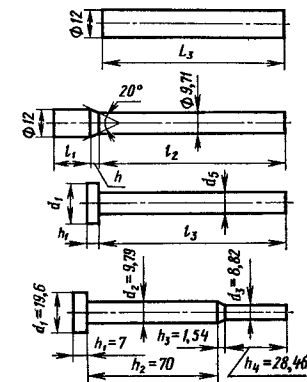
Расчетные схемы заготовки болта М10-100 (а) и выдавленной заготовки (б)
